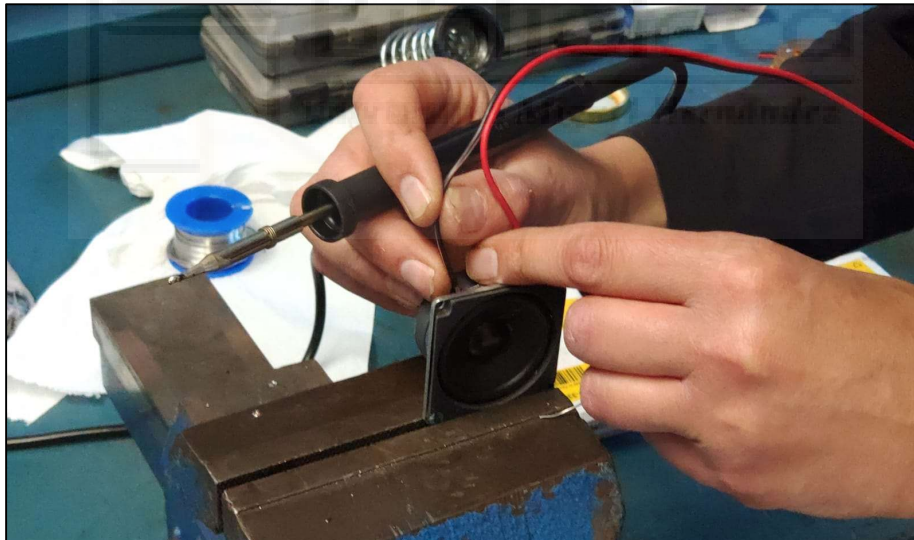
Montaje de los altavoces utilizando soldadura con estaño
